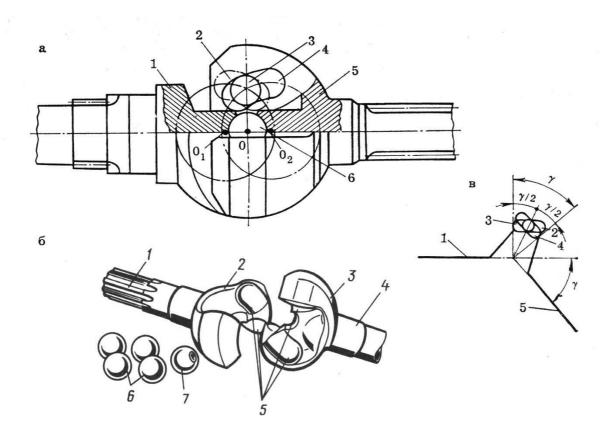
Шариковый шарнир с боковыми делительными канавками:
